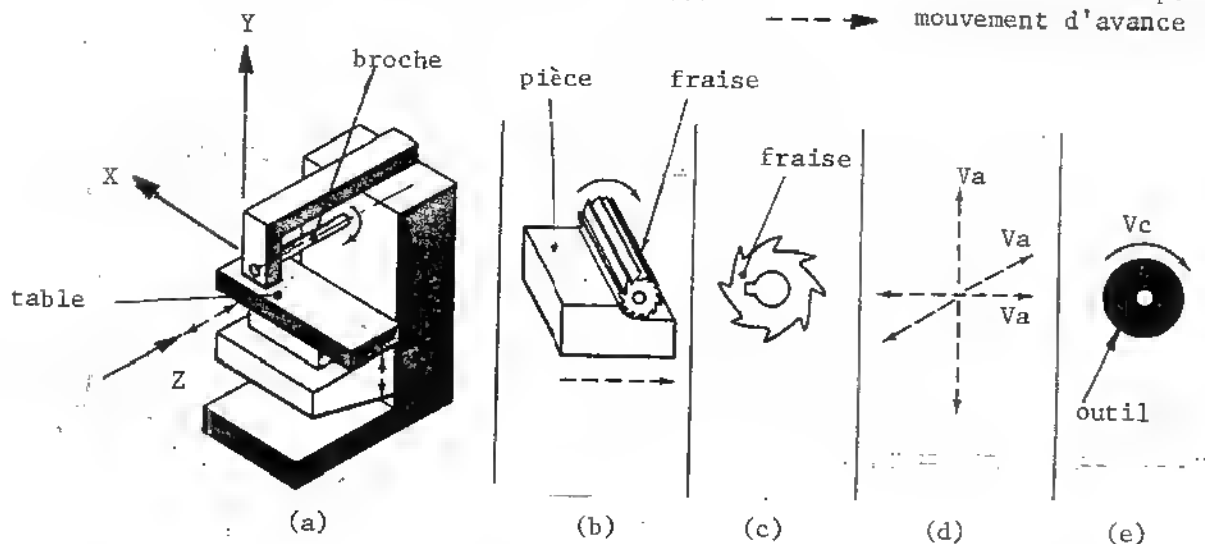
Principe du fraisage horizontal. L'axe de la broche est horizontal.
